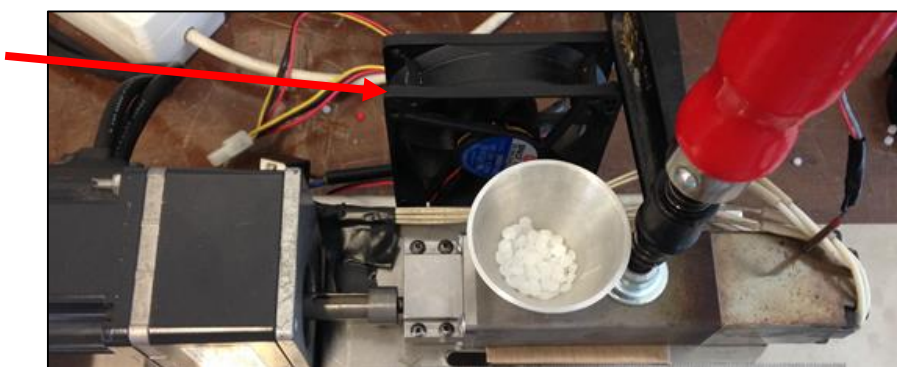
Colocação da ventoinha para arrefecimento da tremonha e zona de alimentação
